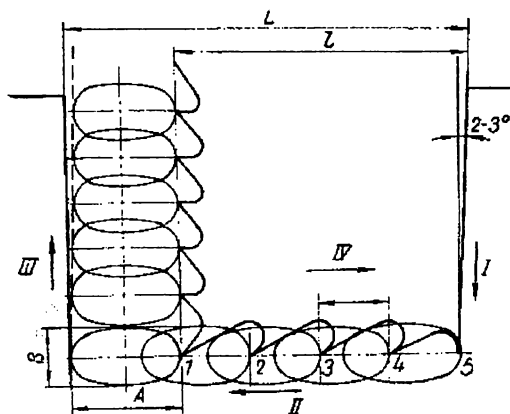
Схема движений зубьев (1-5) гнездовой фрезы
